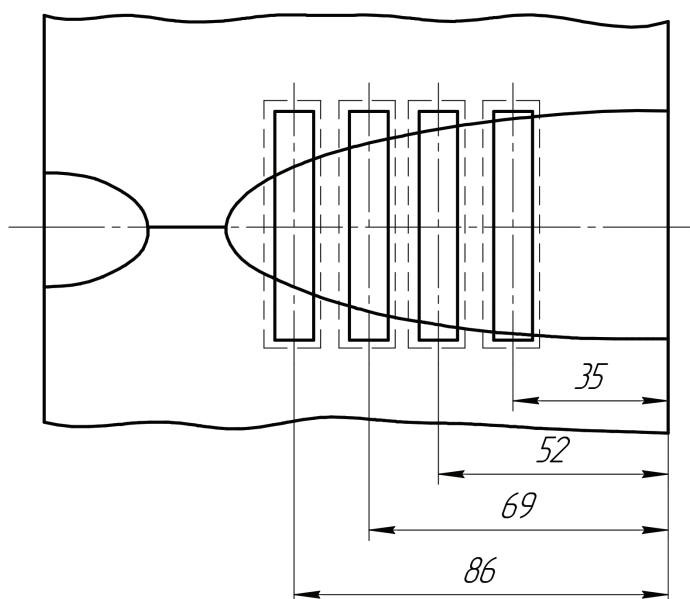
Схема вырезки ударных образцов-свидетелей металла сварного шва
